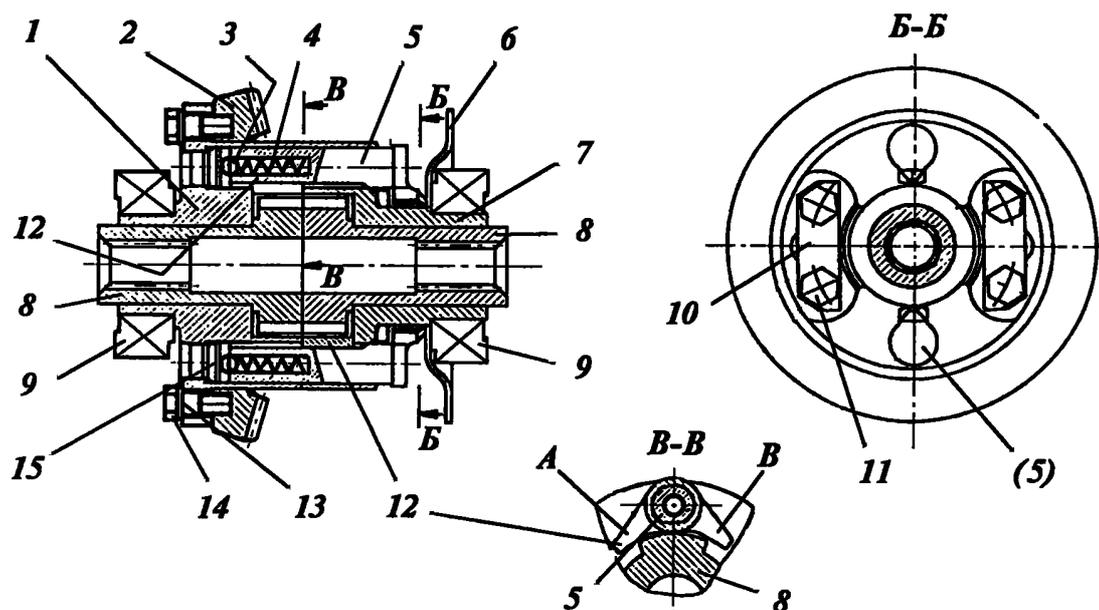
Дифференциал: 1, 7 - фланцы; 2 - шестерня ведомая; 3 - шарик; 4 - пружина; 5 - ось; 6 - диск; 8 - муфта дифференциала; 9 - подшипник; 10, 14 - шайбы; 11 - болт; 12 - собачка; 13 - болт; 15 - заглушка
